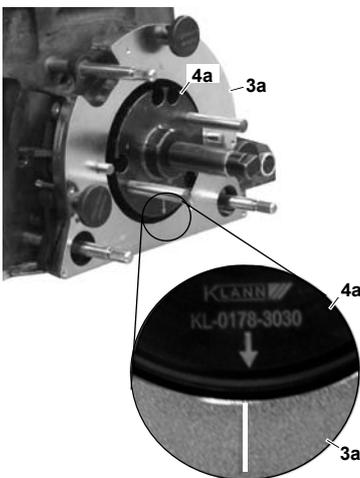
Dichtflansch mit Druckplatte auf Führungsbolzen ansetzen.
